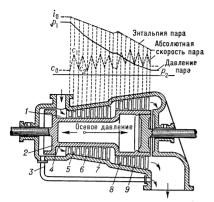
Схематический разрез небольшой реактивной турбины: 1 — кольцевая камера свежего пара; 2 — разгрузочный поршень; 3 — соединительный паропровод; 4 — барабан ротора; 5, 8 — рабочие лопатки; 6, 9 — направляющие лопатки; 7 — корпус.
